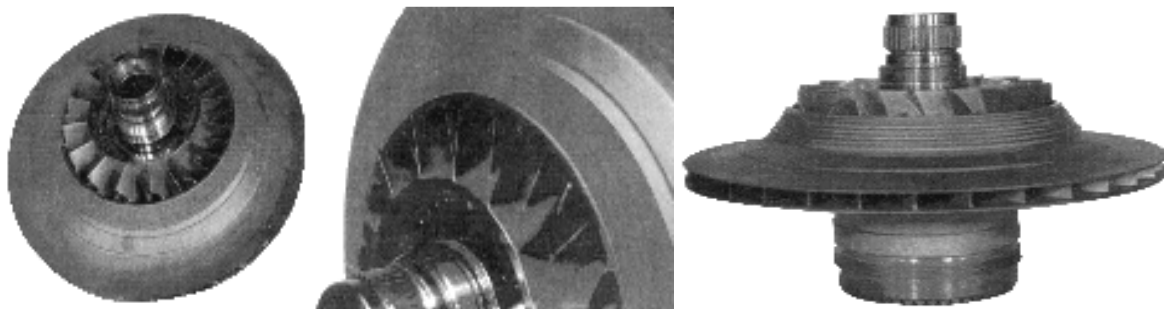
Виды первого варианта готовой детали закрытого центробежного колеса без охлаждения покрывного диска
